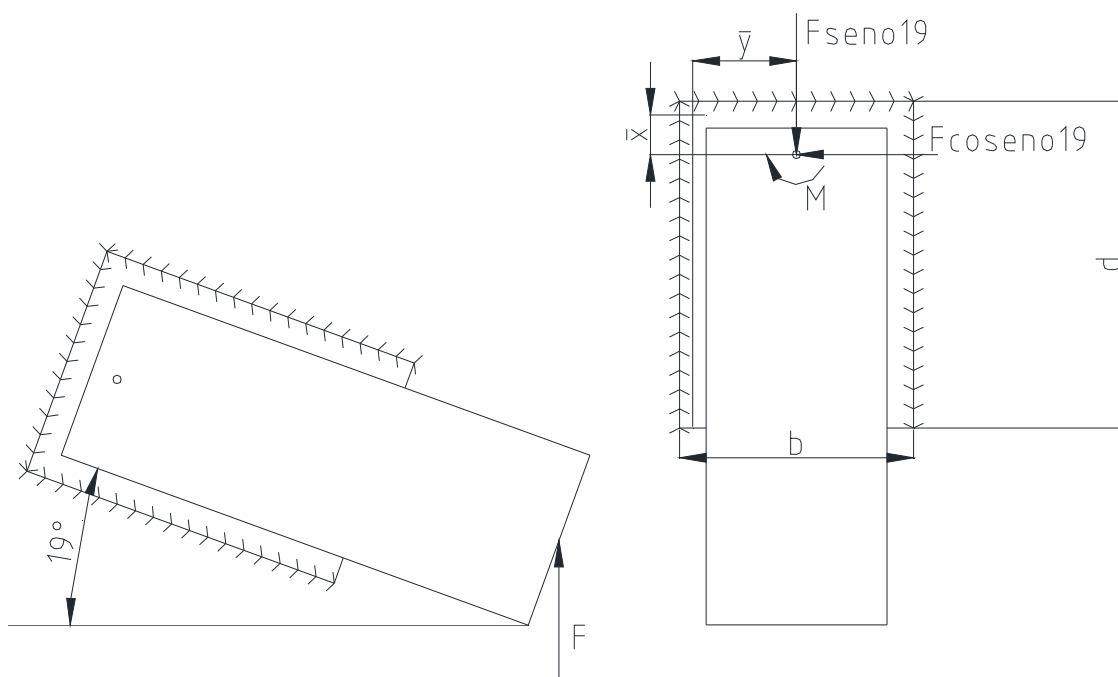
Soldadura de estabilizadores.
